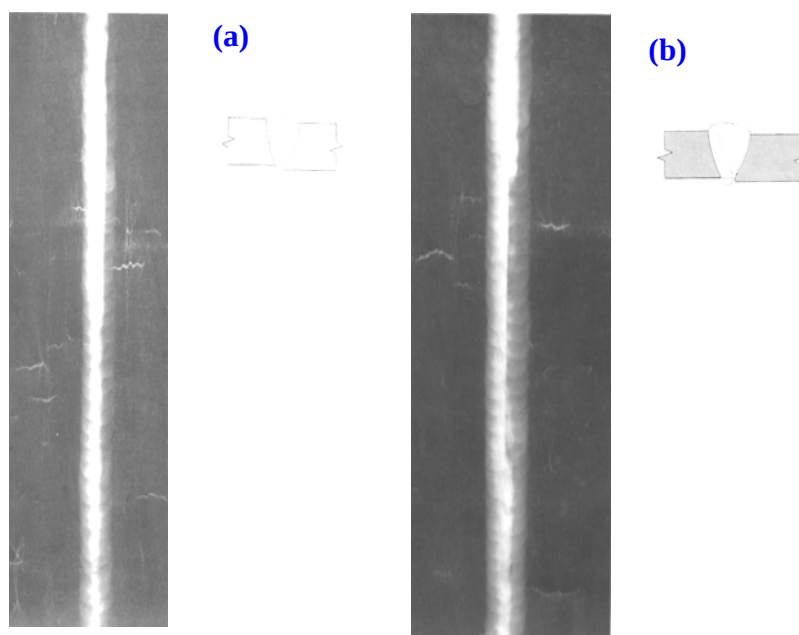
Radiografía Industrial de la Junta Soldada
